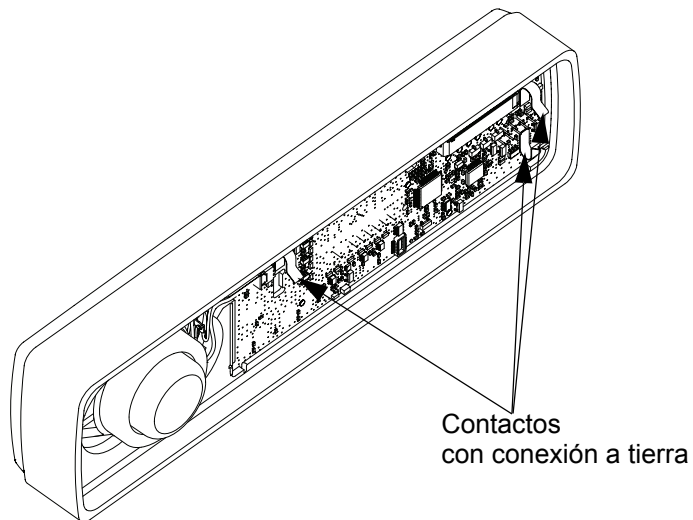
Montaje del teclado en la carcasa del cabezal
